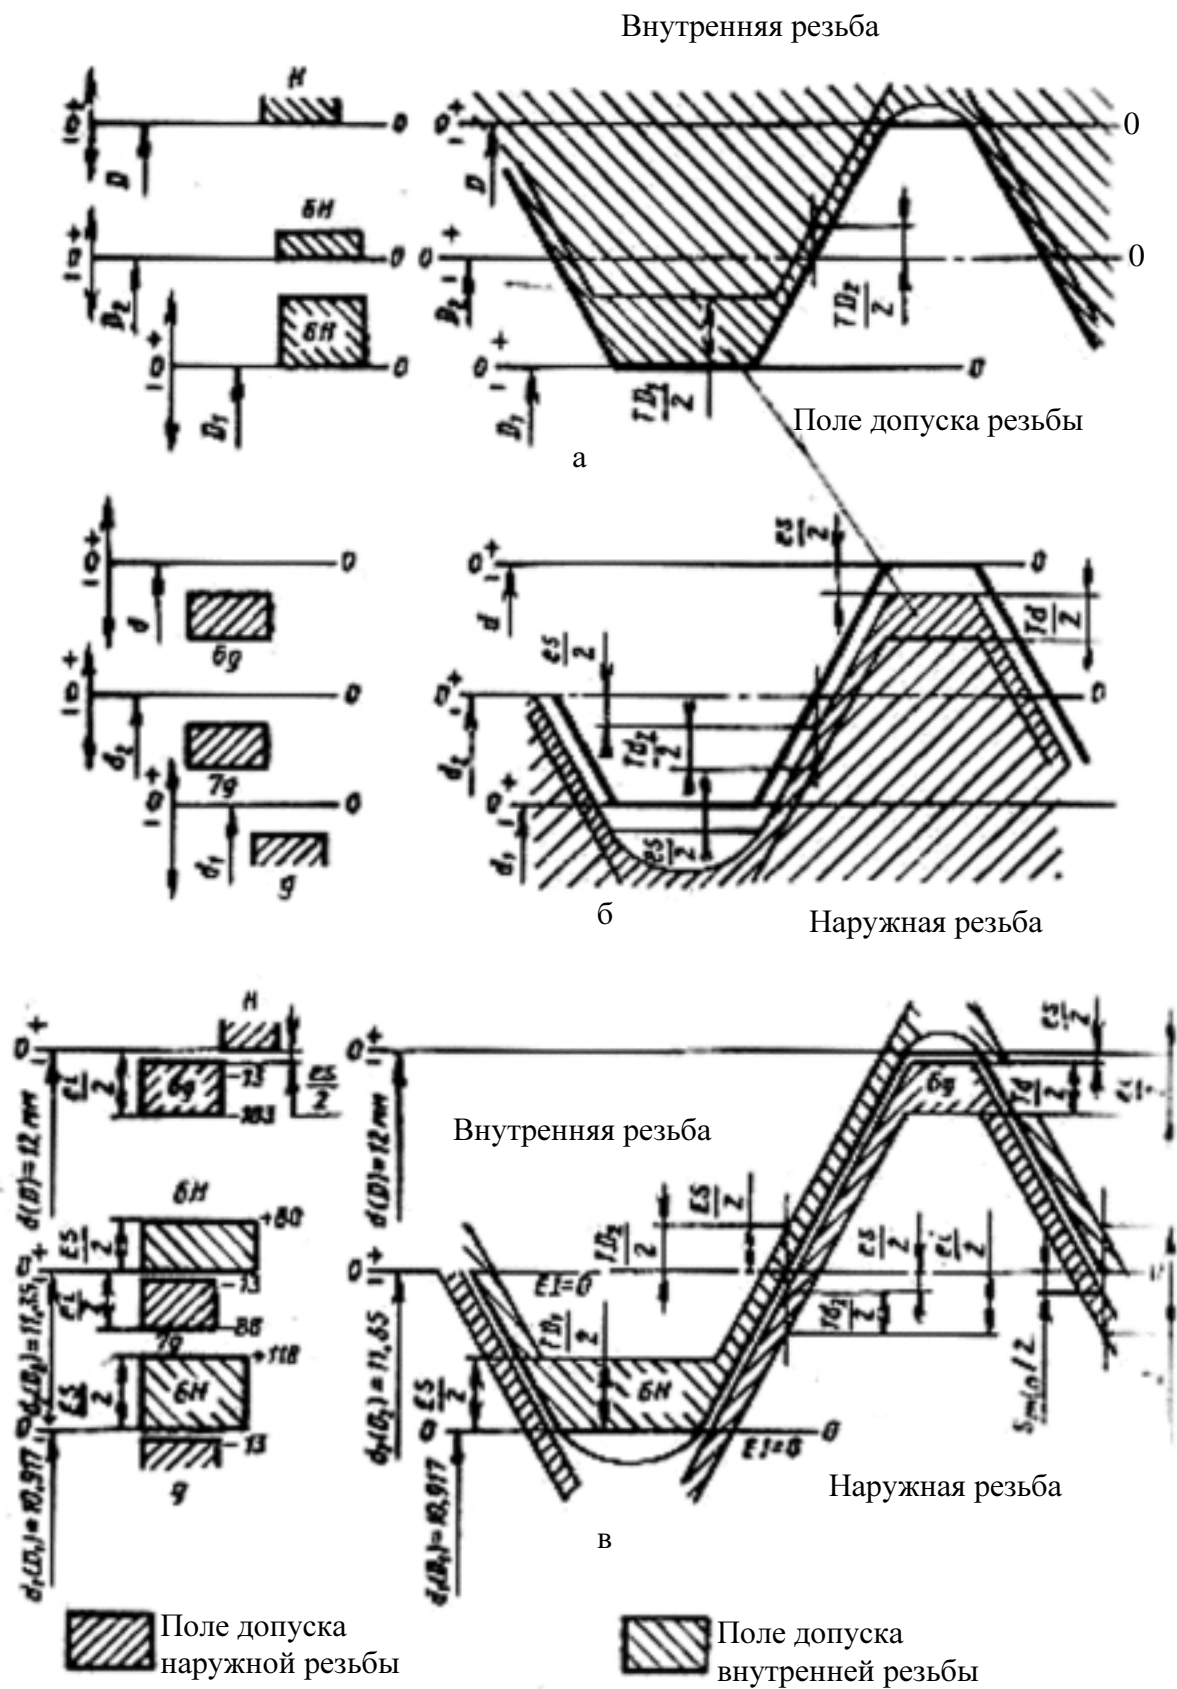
Схемы расположения полей допусков внутренней резьбы (а), наружной резьбы (б) и соединения (в)
